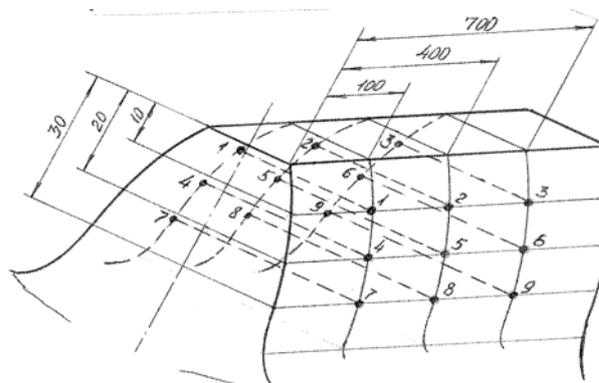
Схема положений измеряемых длин хорд зубьев шестерни
